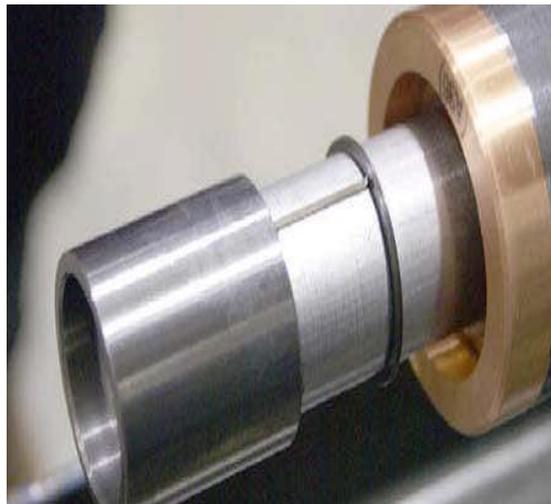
Buje de carburo de tungsteno en el extremo del eje
